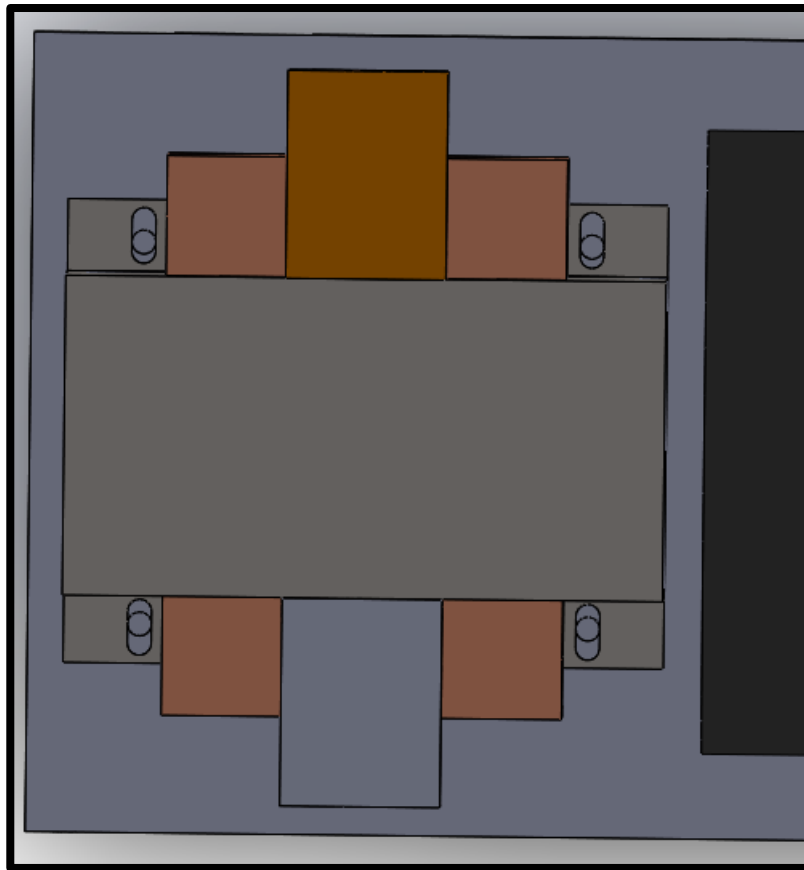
Vista superior de la posición del transformador antes de ser atornillado. Fuente: Propia.
